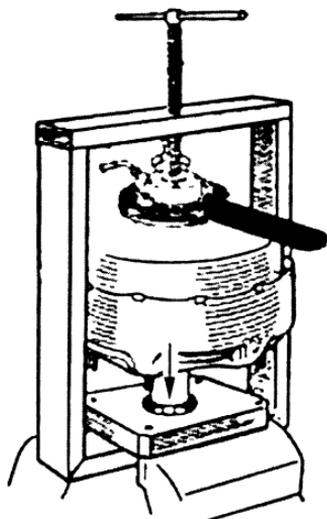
Приспособление для разборки (сборки) гидровакуумного усилителя
